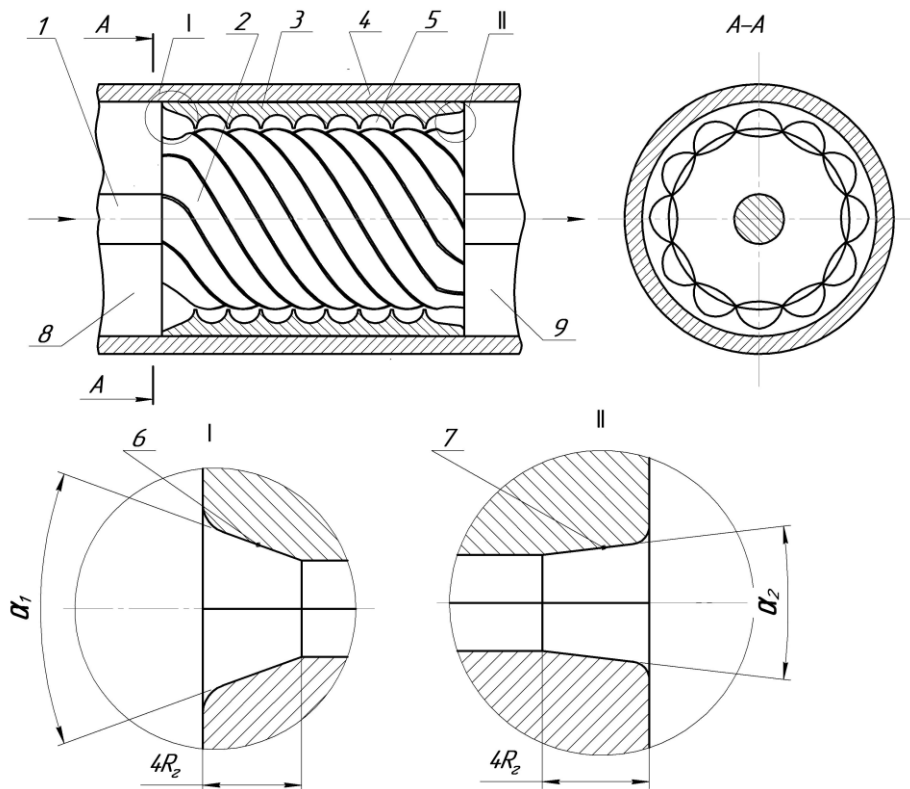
ЛГН з удосконаленою формою робочих органів: 1 – привідний вал; 2 – гвинт; 3 – втулка; 4 – корпус; 5 – гвинтова канавка; 6 – фаска біля вхідної порожнини; 7 – фаска біля вихідної порожнини; 8 – камера підведення; 9 – камера відведення
